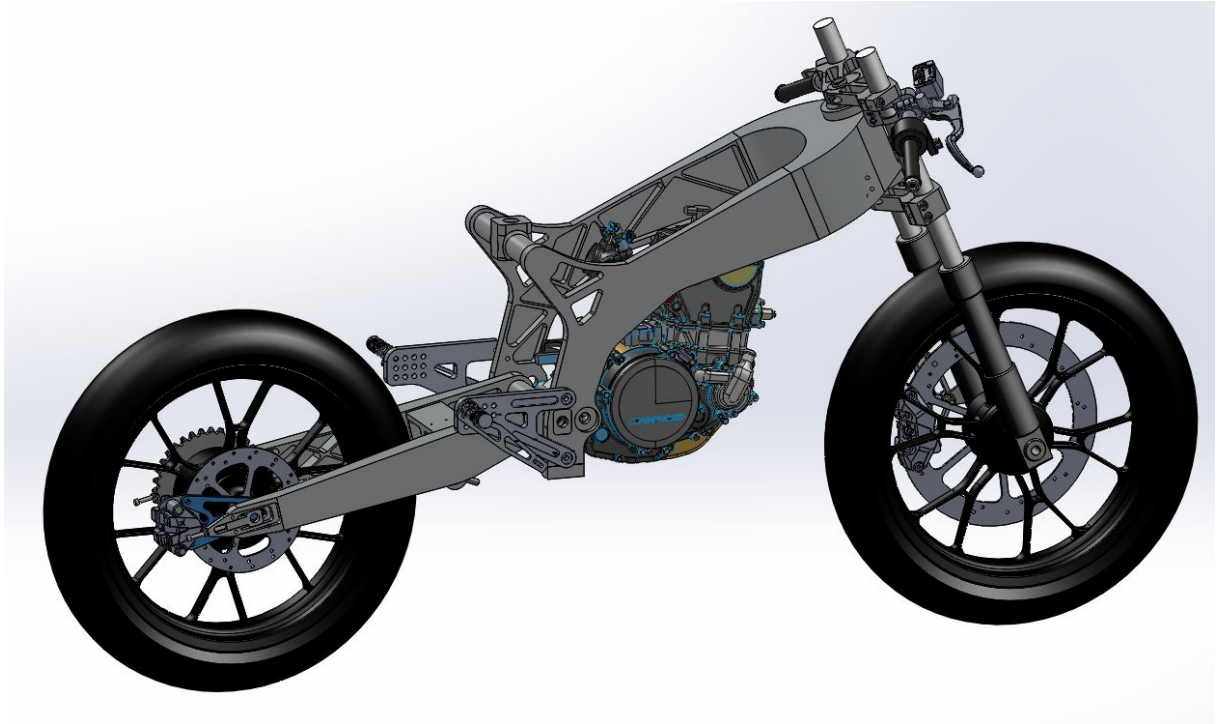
Fabricación. Ensamblaje. Vista general.
